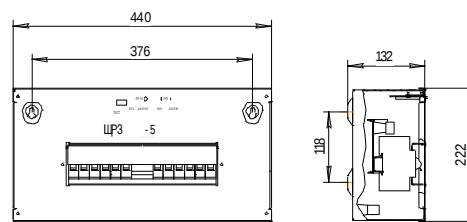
Габаритный чертеж ЩРЗ-5-2 (элементы крепления к стойке не показаны)
